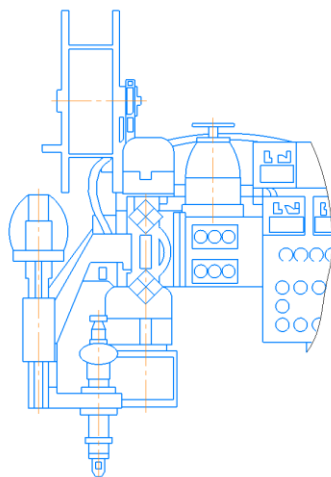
Сварочная головка АСГВ – 4
